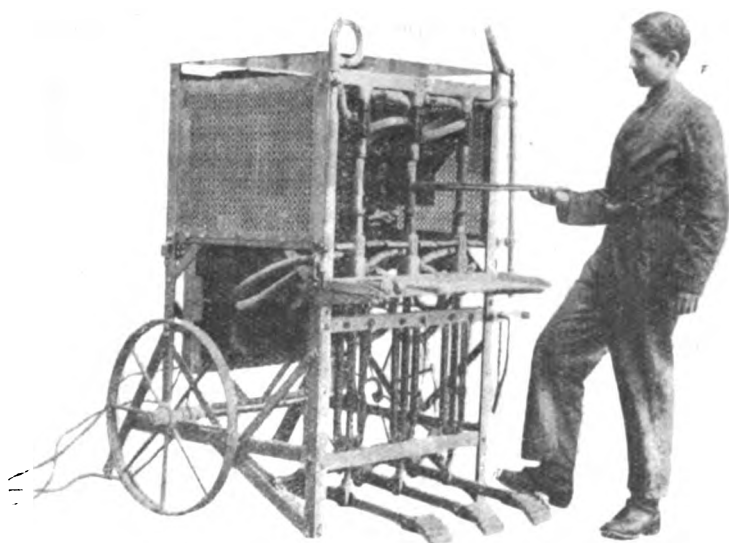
Vue d'une machine électrique à chauffer les rivets (La Soudure électrique).
